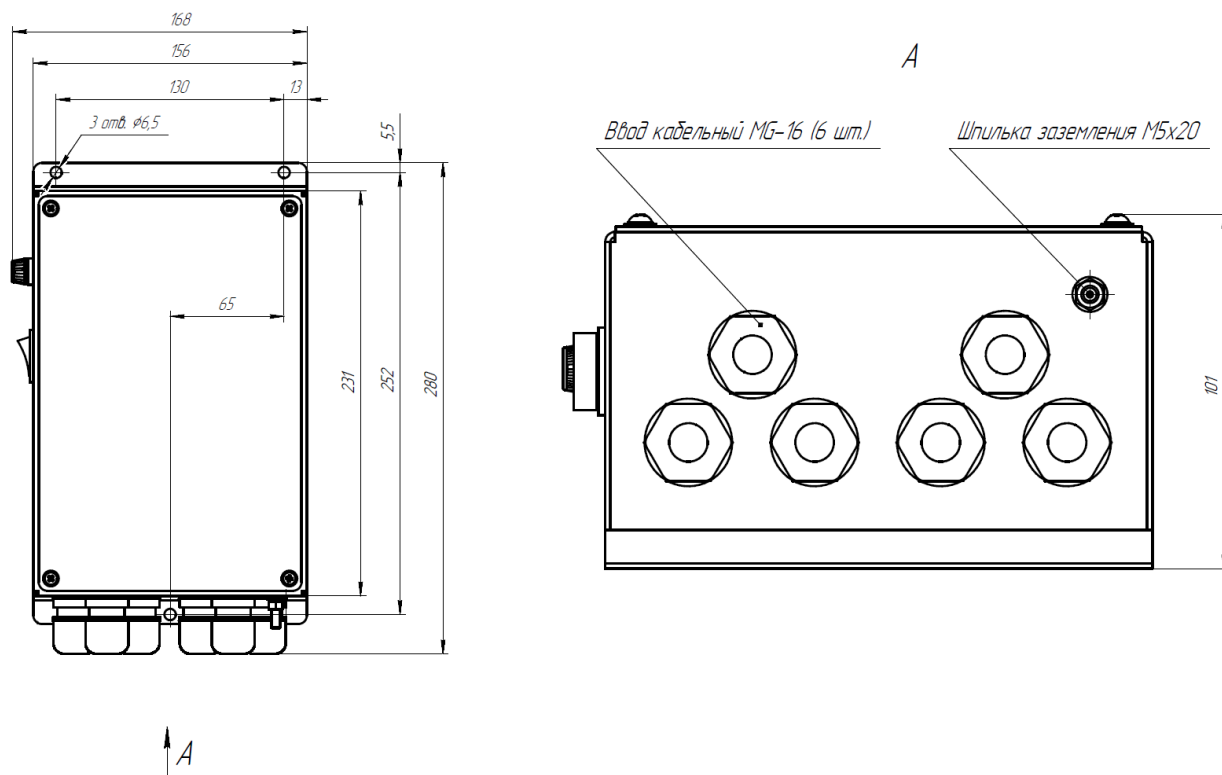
Габаритные и установочные размеры БП-НТИ-24
